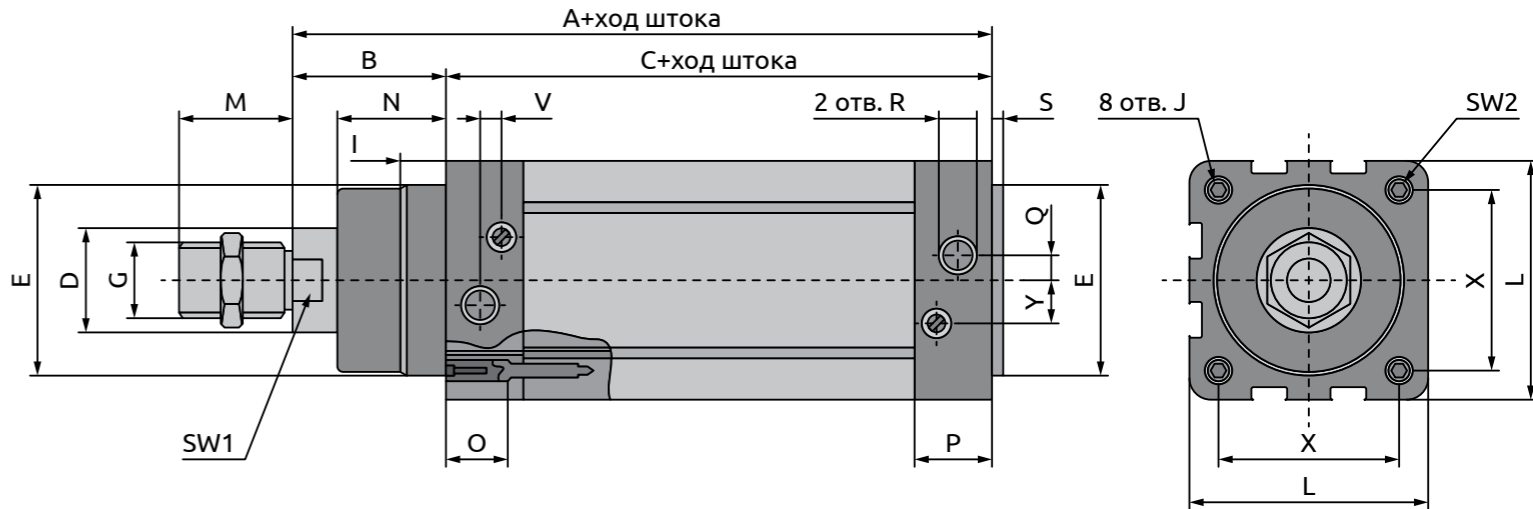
Габаритные размеры пневмоцилиндров серии SPC
